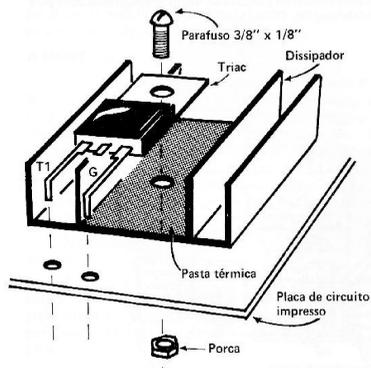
Chapeado da instalação do triac e respectivo dissipador na plaqueta de circuito impresso.
